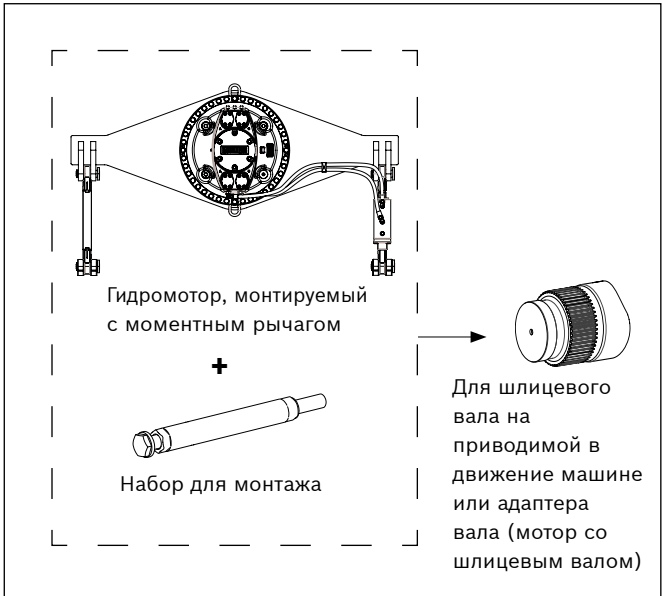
Монтаж с использованием моментного рычага с двумя плечами для шлицевого вала
